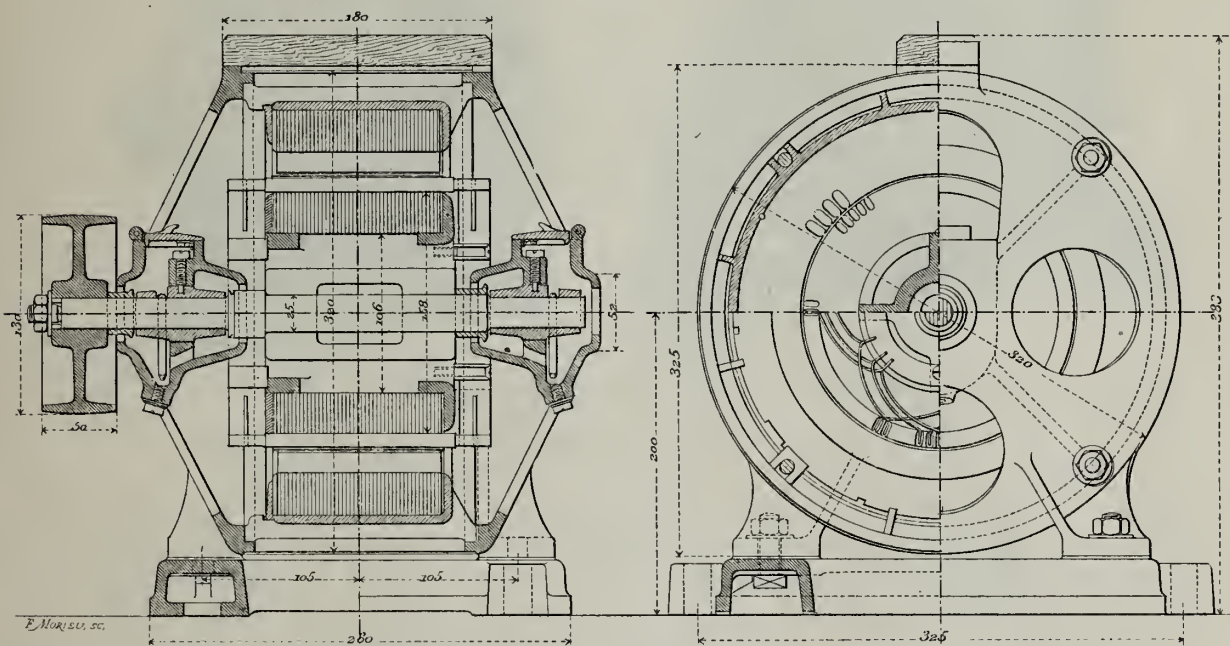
Coupe longitudinale. — FIG. 45. — Vue par bout avec coupe transversale partielle.
